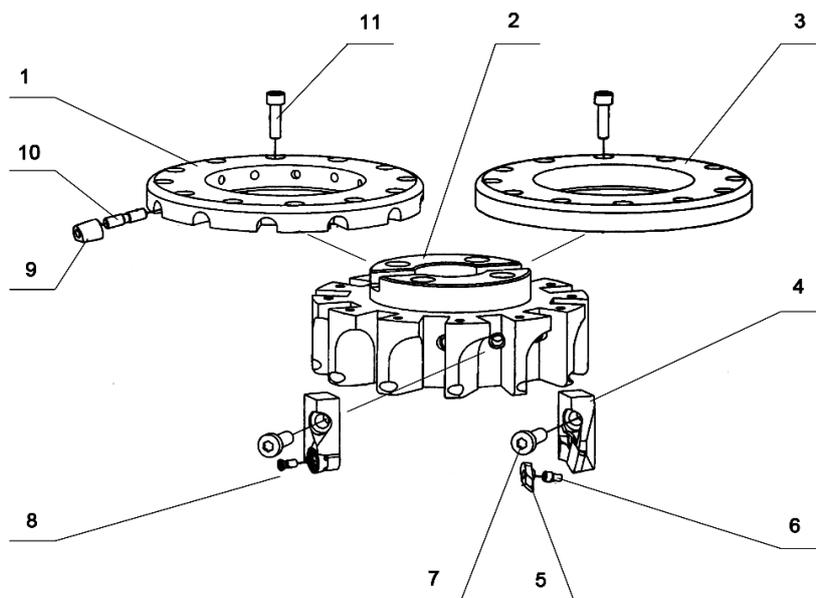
Технологическая схема сборки фрезы фирмы ОАО «Специнструмент»: 1 – регулирующее фиксирующее кольцо; 2 – корпус фрезы; 3 – не регулирующее фиксирующее кольцо; 4 – картридж; 5 – Г-образный прихват; 6 – винт крепления Г-образного прихвата; 7 – винт крепления картриджа; 8 – винт крепления пластины; 9 – регулятор картриджа; 10 – винт регулятора картриджа; 11 – винт для крепления кольца
